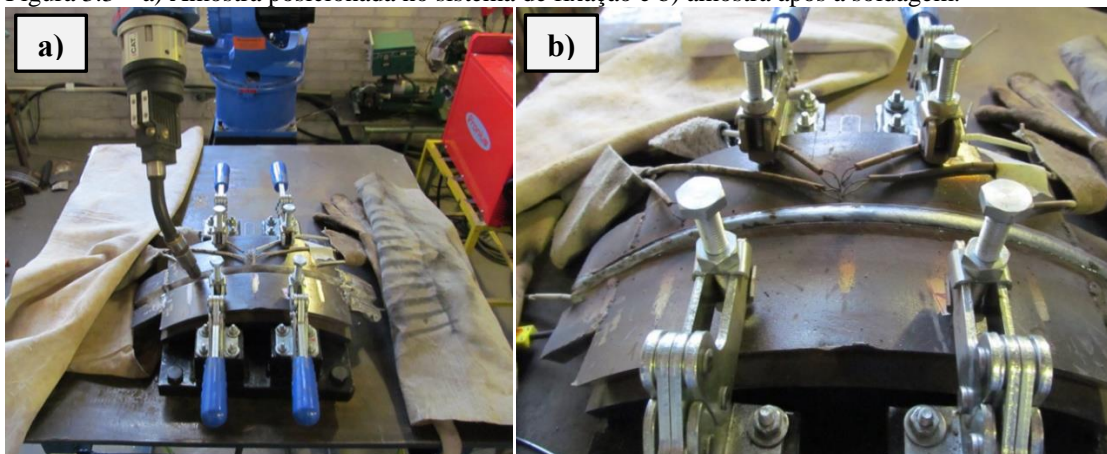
a) Amostra posicionada no sistema de fixação e b) amostra após a soldagem.
